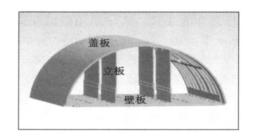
某油箱焊接结构 Fig. 3 Model of oil box
